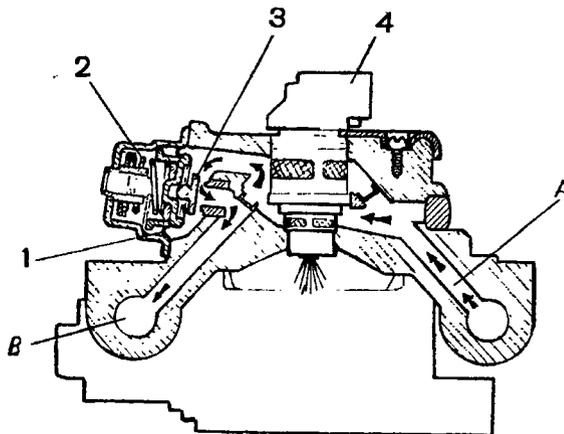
Схема работы регулятора давления топлива: 1 - диафрагма регулятора давления; 2 - пружина; 3 - клапан регулятора давления; 4 - форсунка; А - канал подвода топлива; В - канал слива топлива
